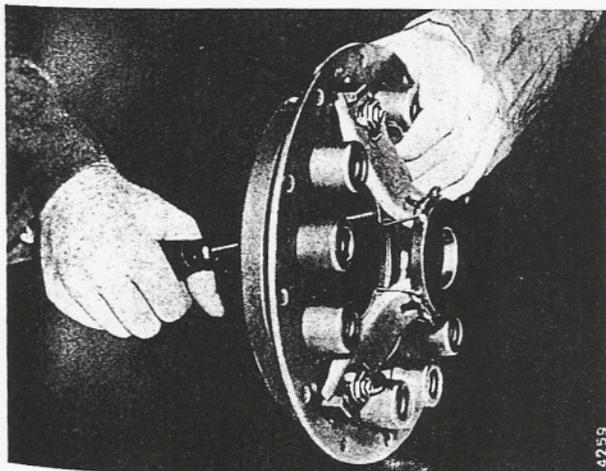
Enlever l'assemblage de pression et le plateau de pression
